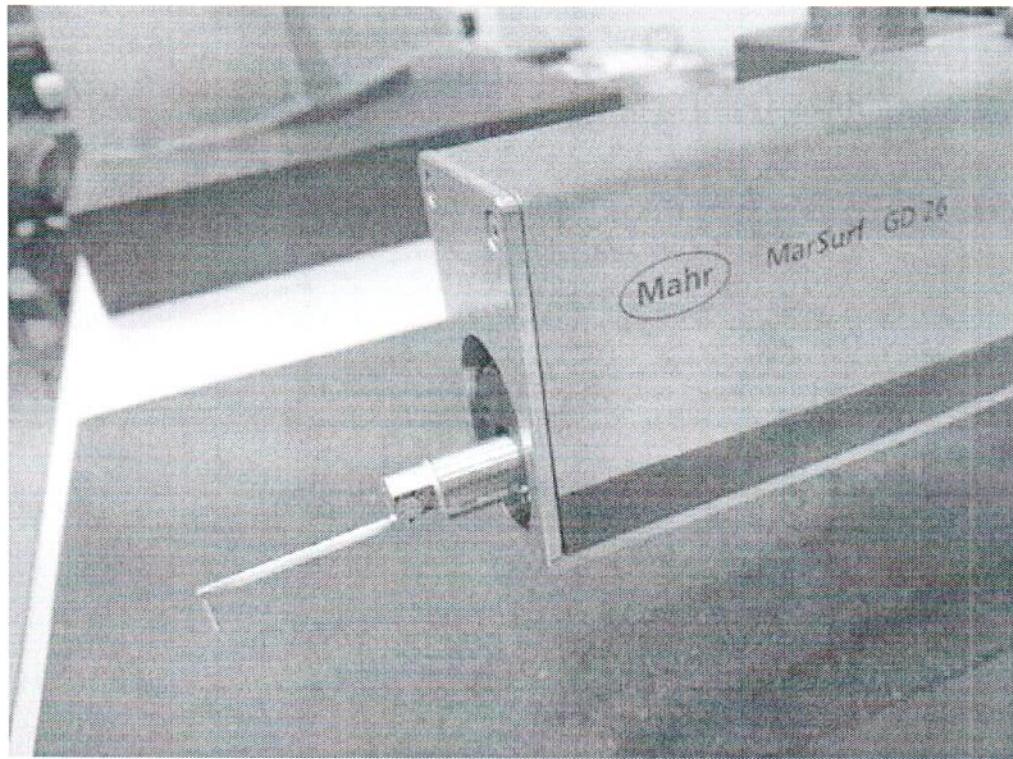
Внешний вид приборов для измерения шероховатости поверхности MarSurf XR1 в составе с GD 26
